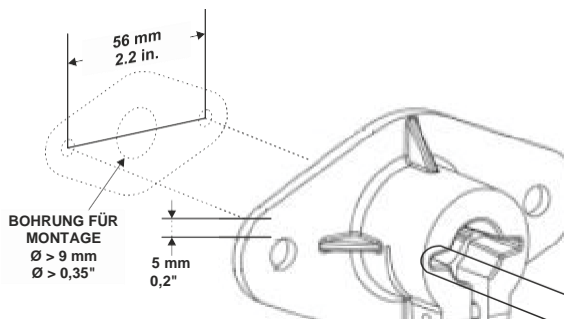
Flanschmontage an Kanal (mm, Zoll)
